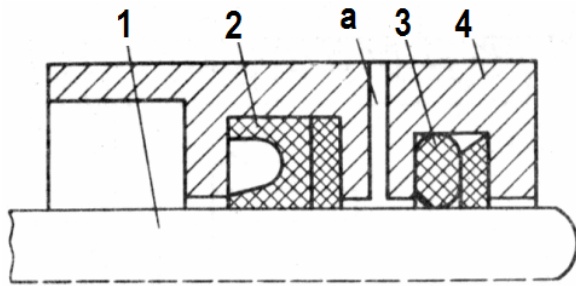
Схема резервирования уплотнения штока гидроцилиндра
